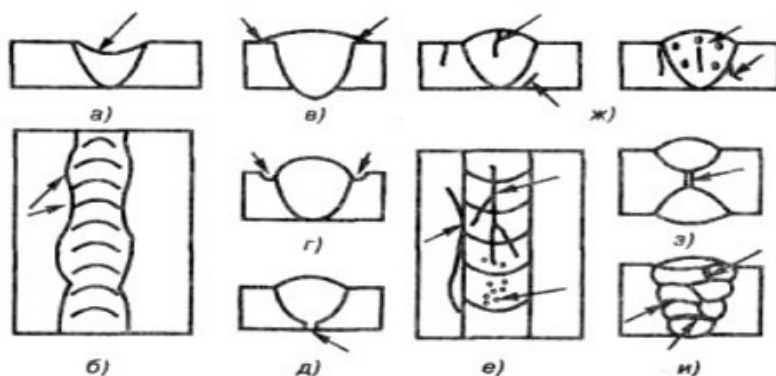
Виды дефектов сварных соединений (где а — ослабление шва, б — неравномерность ширины, в — наплыв, г — подрез, д- непровар, е — трещины и поры, ж — внутренние трещины и поры, з — внутренний непровар, и — шлаковые включения).
